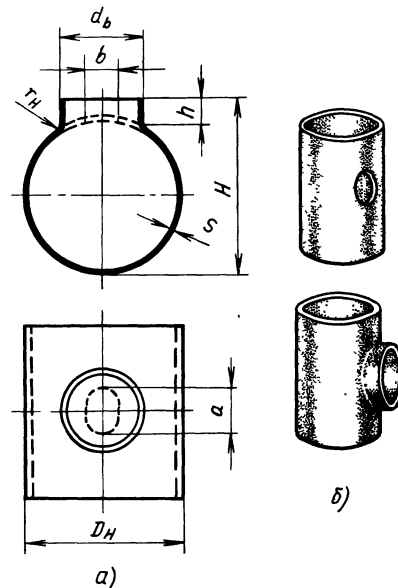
Горловина на цилиндрической пустотелой заготовке
